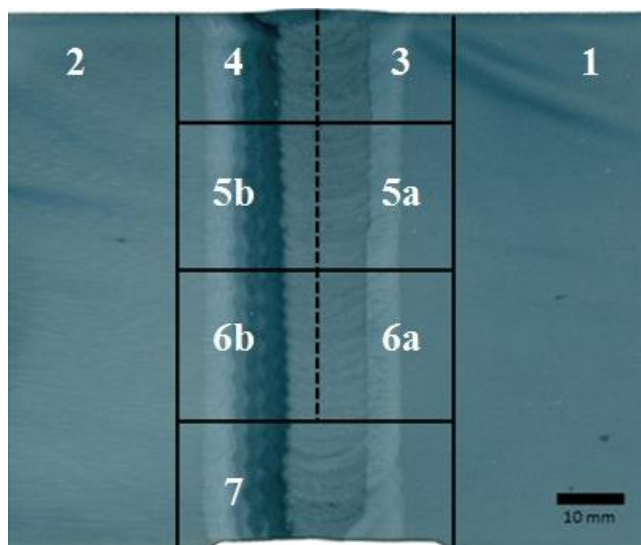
Místo odběru segmentu z rotoru parní turbíny
